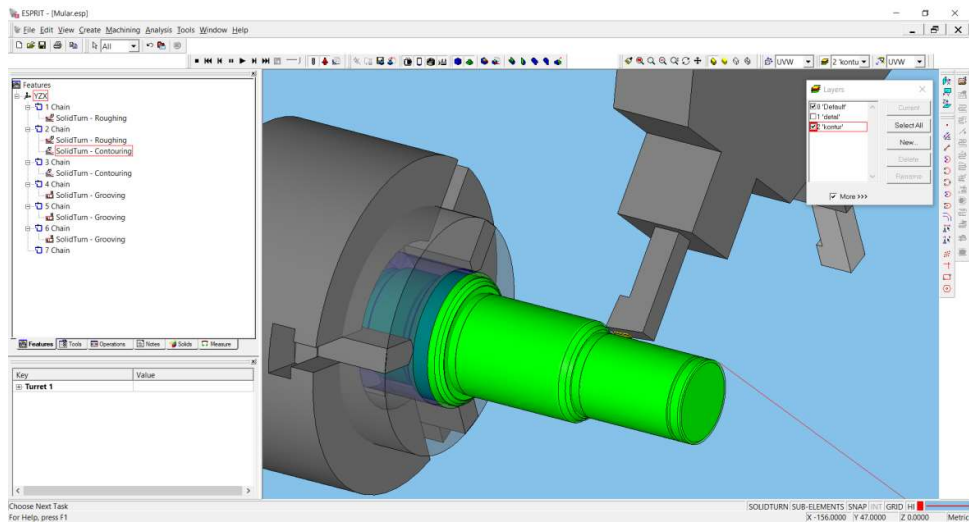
Траєкторія руху металорізального інструменту при обробленні кришки
